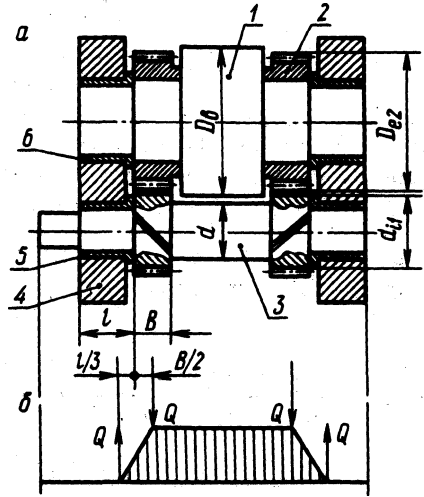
Зубчатая передача рабочей клетки стана для прокатки порошков (а); 1 – валок; 2 – зубчатое колесо; 3 – вал-шестерня; 4 – станина рабочей клетки; 5 – подшипники вала-шестерни; 6 – подшипники валка; эпюра изгибающих моментов вала-шестерни (б).
